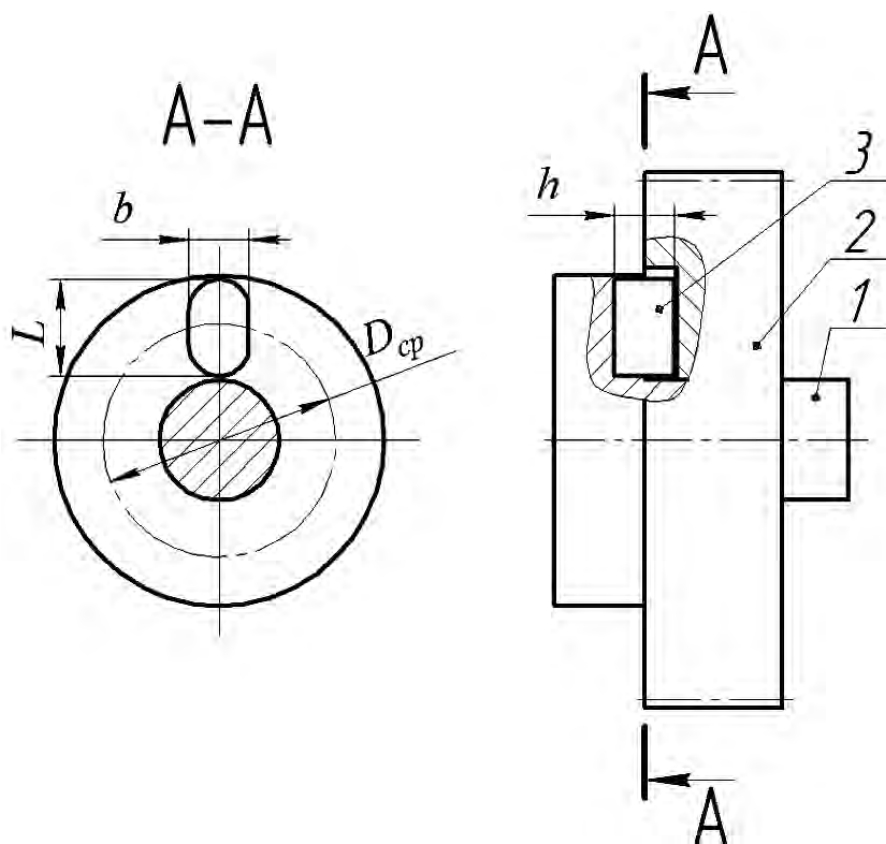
Соединение с помощью шпонки, размещенной на торце вала и ступицы: 1 – вал; 2 – колесо; 3 – шпонка
